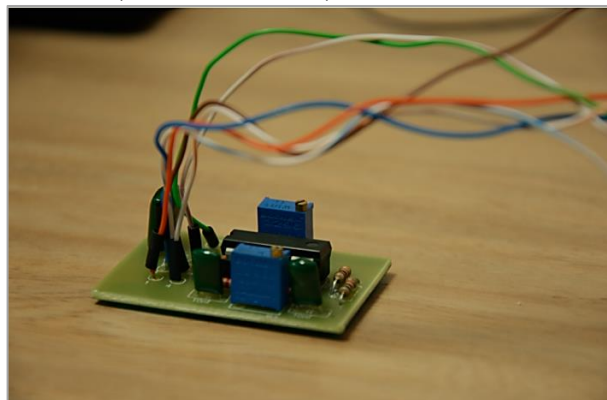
Detalle del Proceso Constructivo de la Caja del Transductor de Presión Soldado de Conectores
